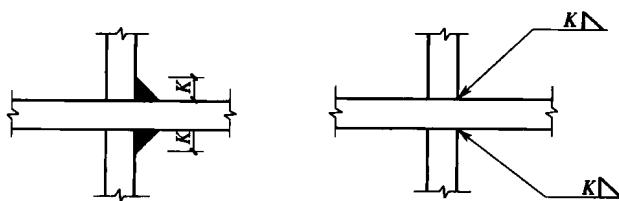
3个和3个以上焊件的焊缝标注方法
